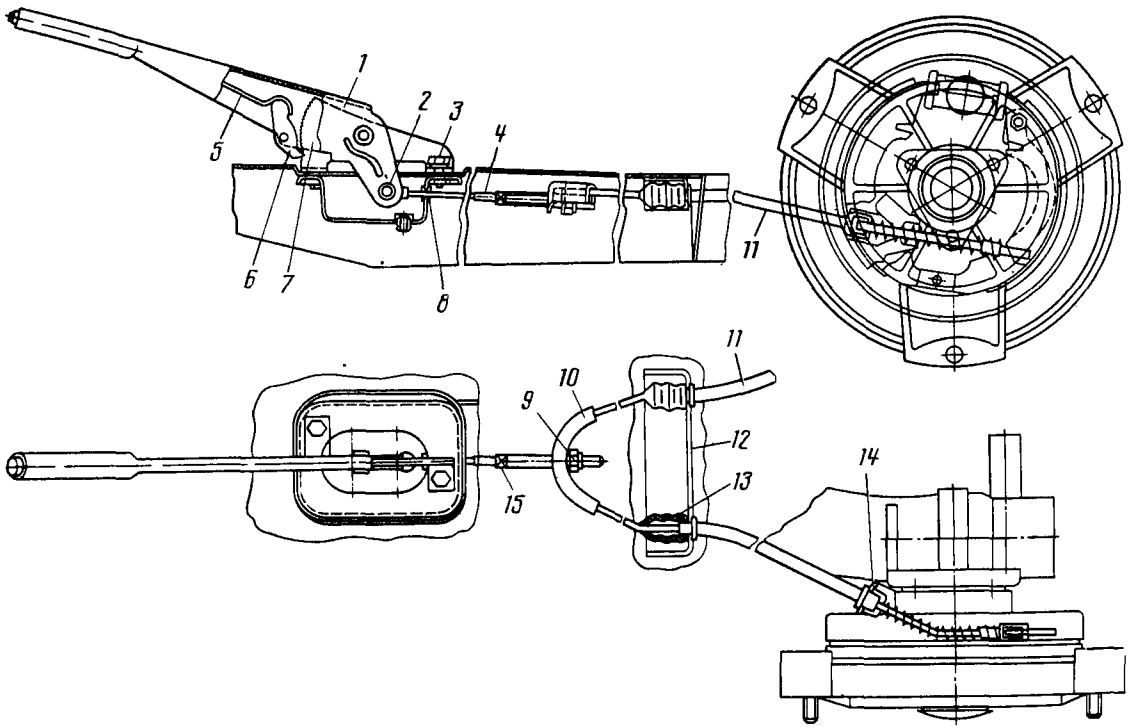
Стояночный тормоз и его установка на автомобиль:
